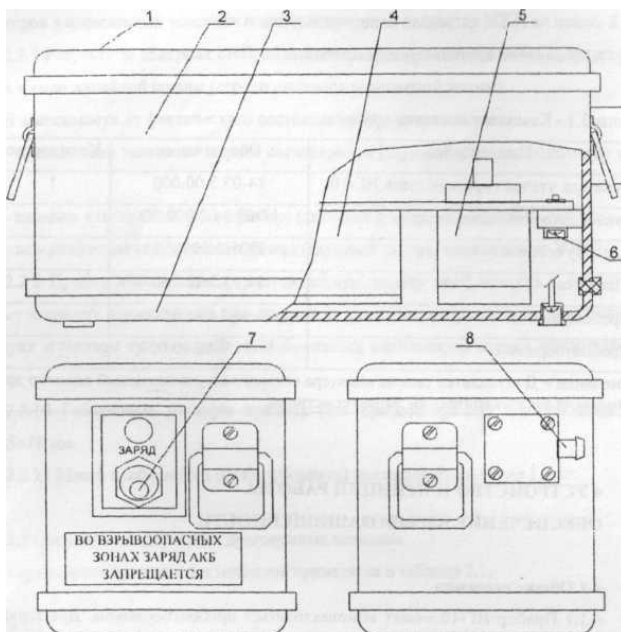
Внешний вид прибора: 1 – панель управления; 2 – корпус; 3 – съёмная нижняя крышка; 4 – отсек аккумуляторов; 5 – камера измерительная; 6 – место пломбирования; 7 – гнездо подключения сетевого адаптера и индикатор процесса зарядки аккумуляторов; 8 – штуцер подключения трубки пробоотборника
